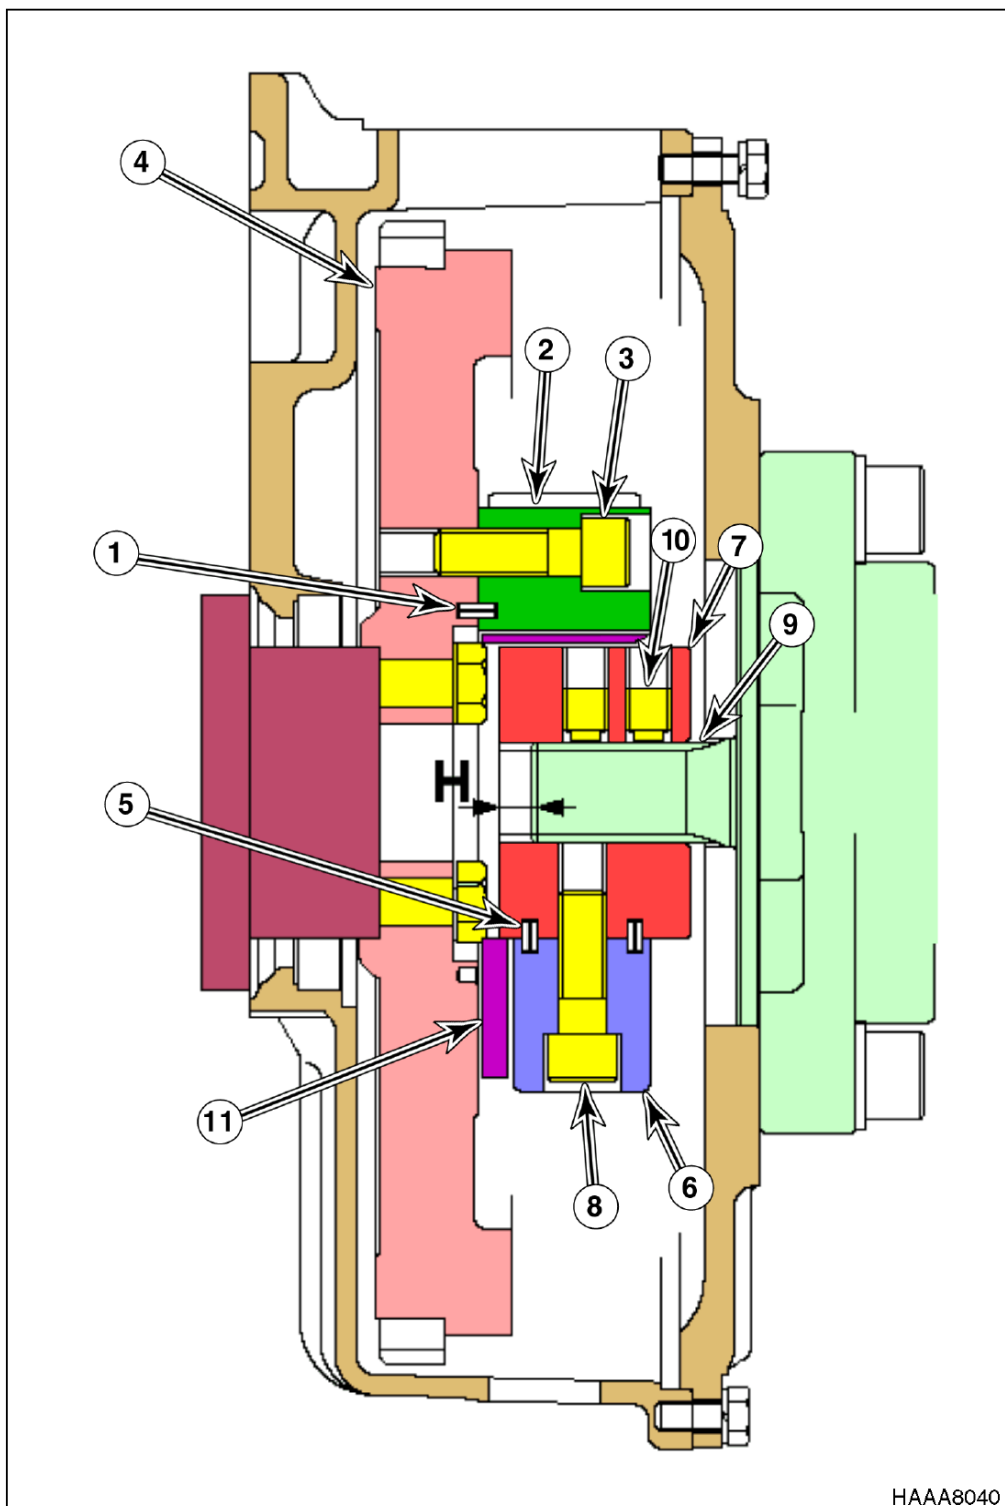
УСТАНОВКА МУФТЫ ПРИВОДА
